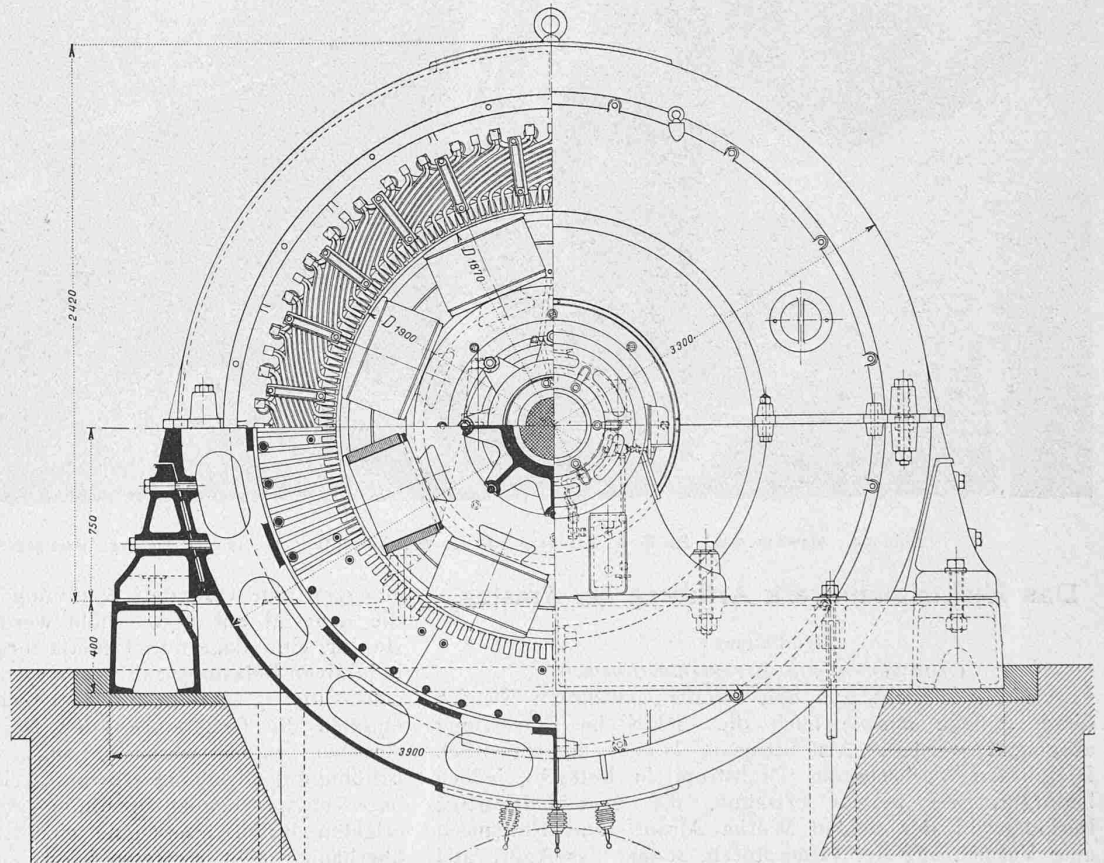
Drehstromgenerator für 2600 KVA, 4150 V, 42 ∞, 630 Uml/min. — Ansicht und Schnitt 1:30.
